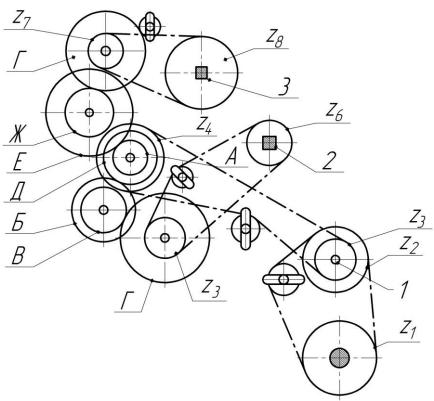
Схема привода зерновой сеялки СЗ-3,6: вид слева.
